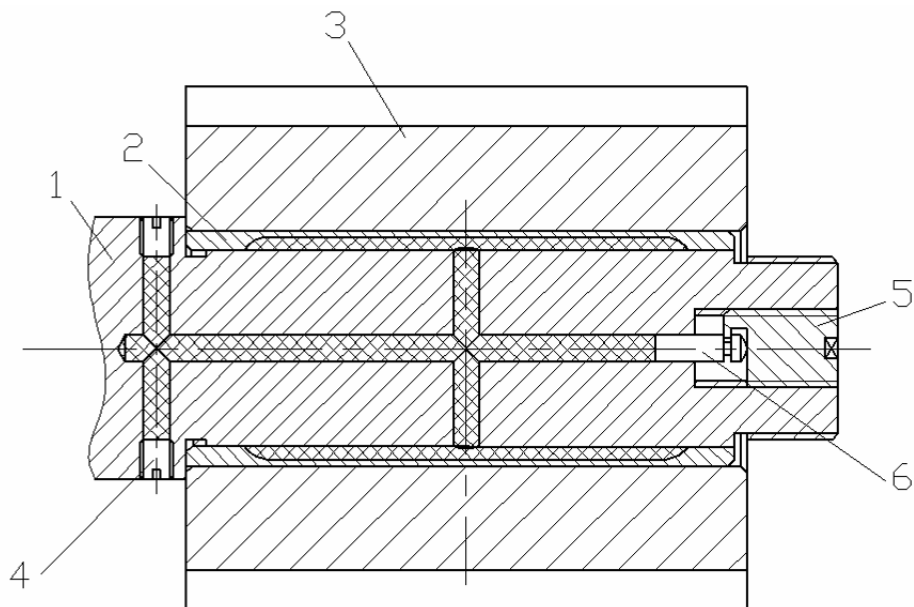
Схема установки фрезы за счет самоцентрирующейся втулки
